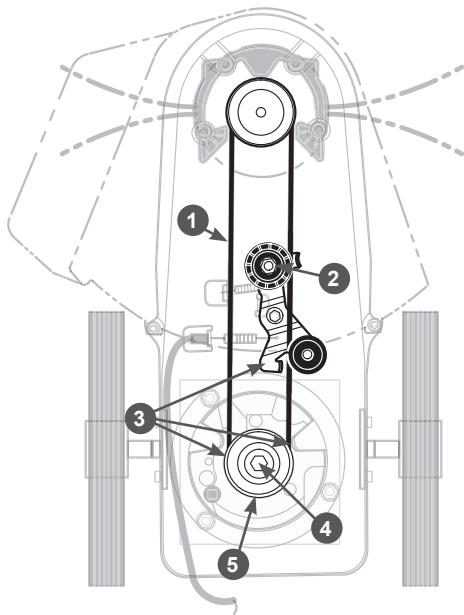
Снятие защитного кожуха и корпуса триммерной головки
